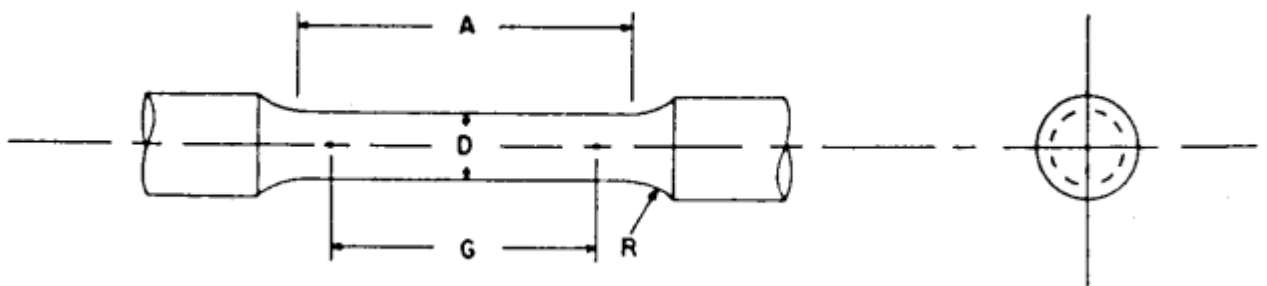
Dimensions d'éprouvette Ronde standardisée
